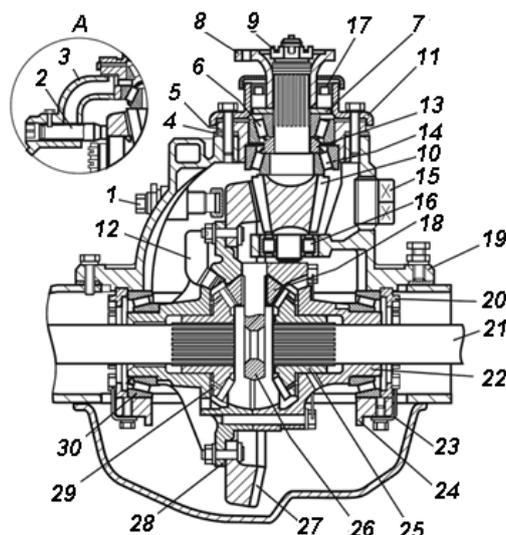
Редуктор заднего моста автобуса ПА3-32053 (1 – винт регулировочный; 2 – втулка; 3 – верхний канал; 4 – регулировочные прокладки; 5 – муфта; 6, 14, 16, 30 – подшипники; 7 – кольцо маслоотгонное; 8 – фланец; 9 – гайка; 10 – шестерня ведущая; 11 – крышка; 12 – маслоуловитель; 13 – кольцо регулировочное; 15 – пробка заливного отверстия; 17 – манжета; 18 – сателлит; 19 – картер; 20 – гайка; 21 – полуось; 22, 28 – коробки сателлитов; 23 – стопорная пластина; 24 – крышка; 25 – шестерня полуоси; 26 – крестовина; 27 – шестерня ведомая; 29 – шайба опорная; А – сечение по масляному каналу подшипников ведущей шестерни)
